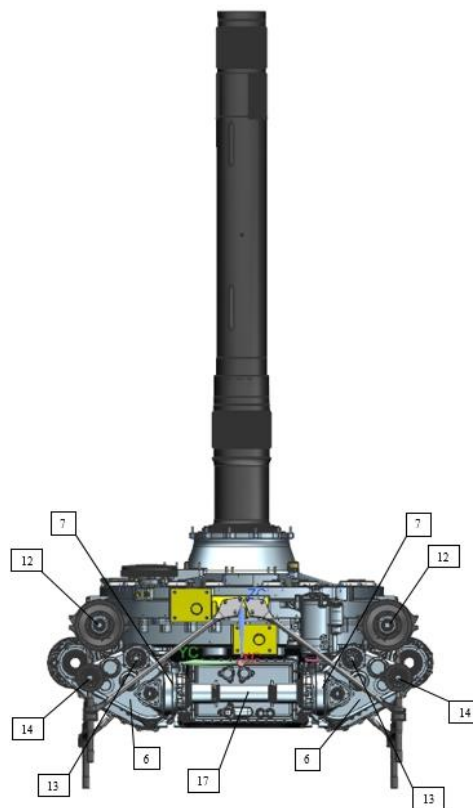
Главный редуктор ВР-450, вид сзади
